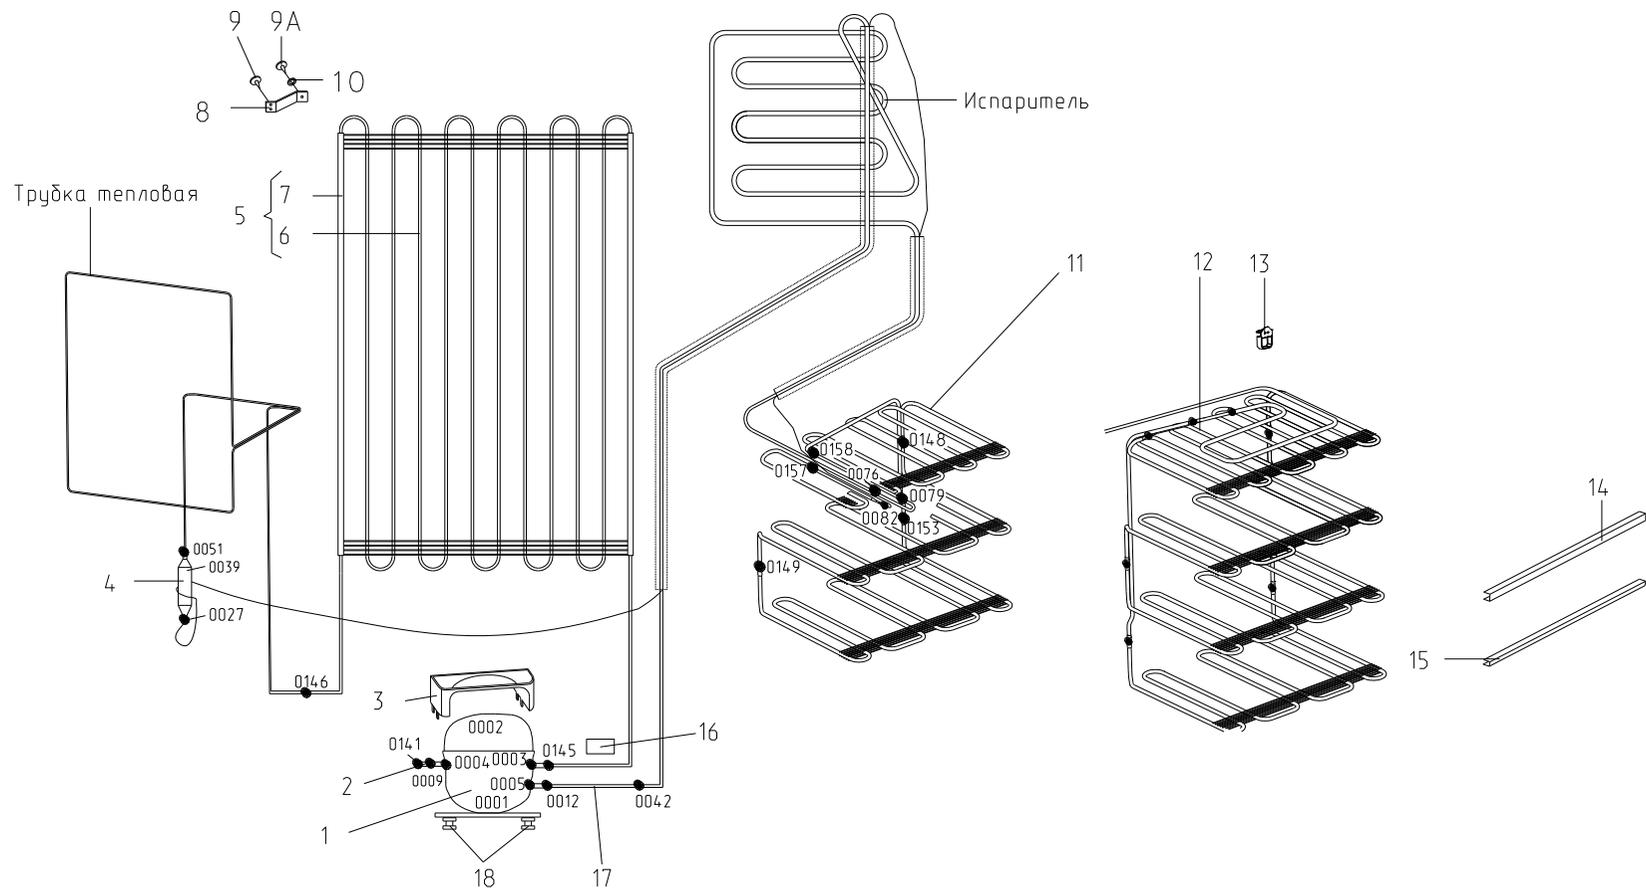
Схема холодильного агрегата (компрессор типа С-КН)
